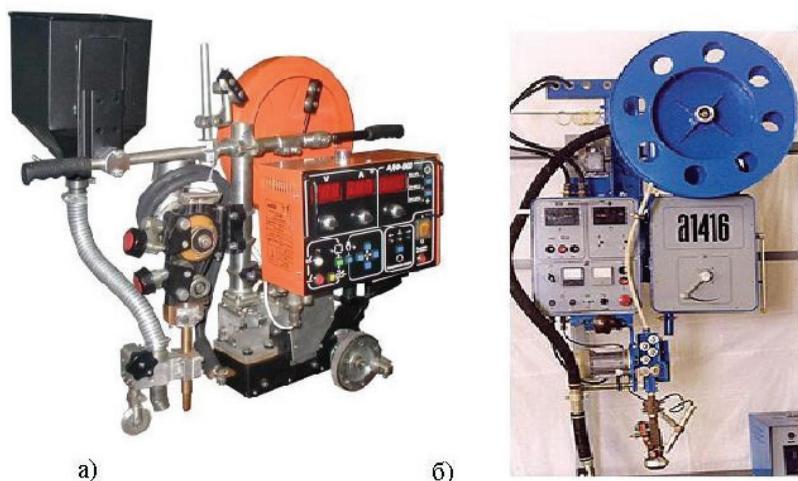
Сварочный трактор АДФ-800 (а)
